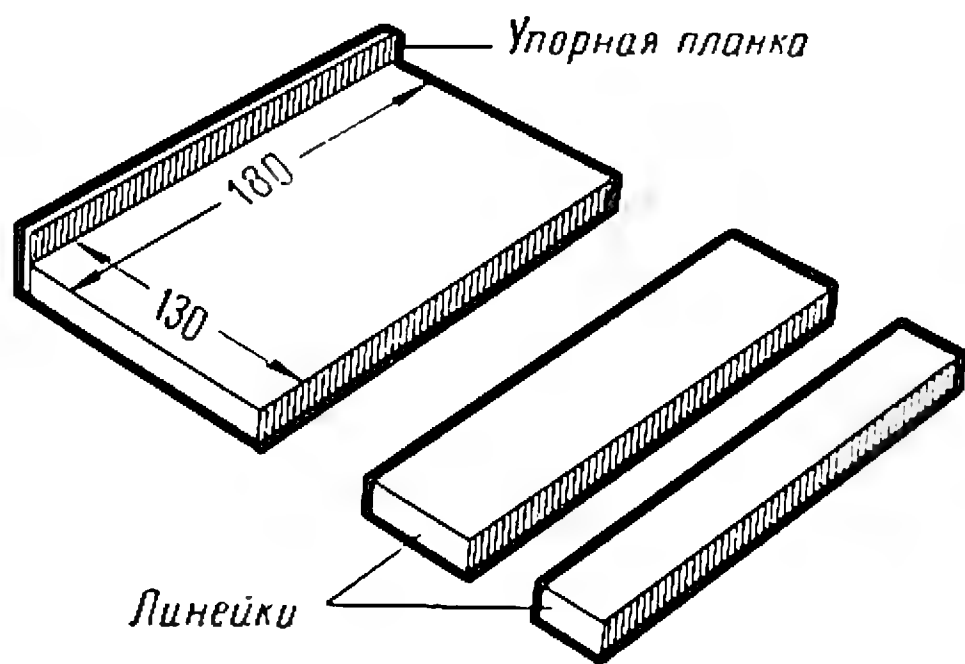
Станочек для нарезки диапозитивных фотопластинок
